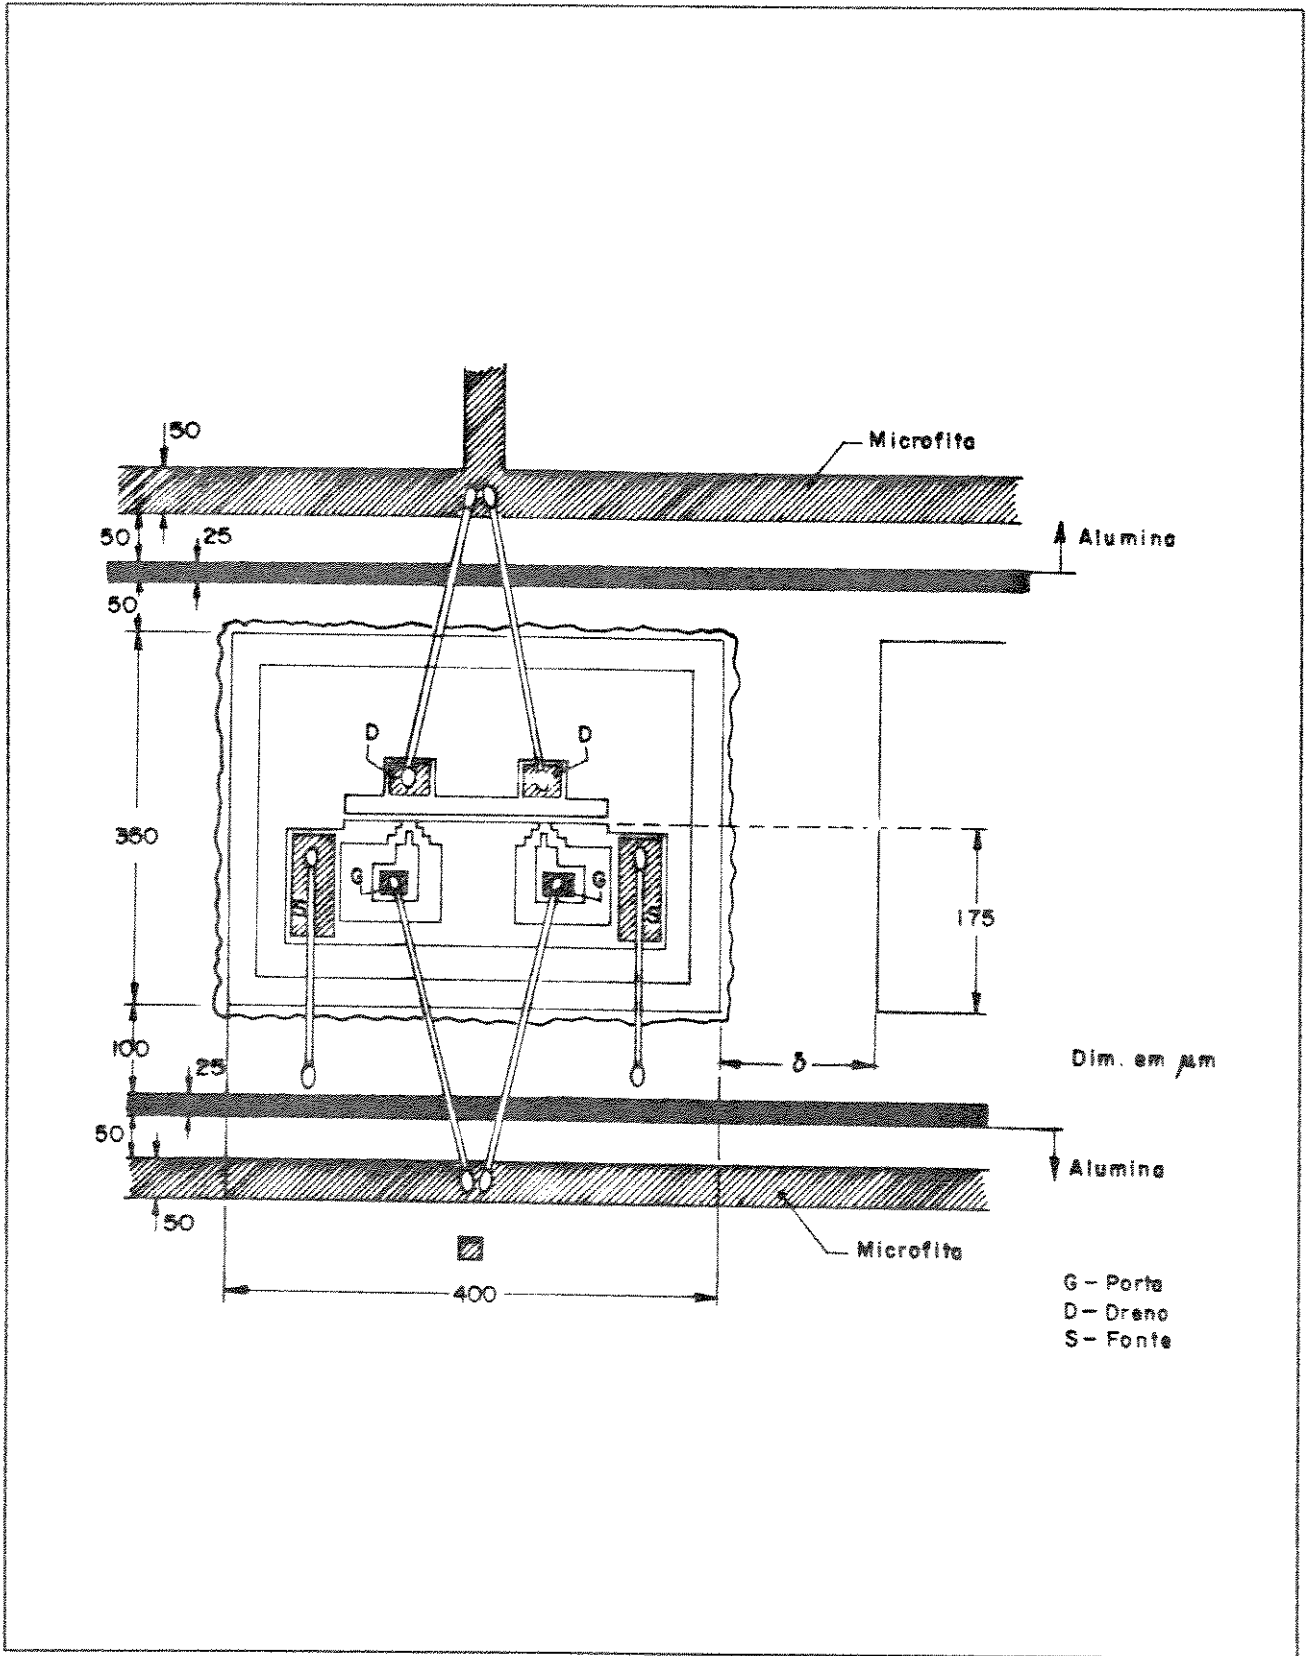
Detalhe das soldas de fios do HEMT NE32100, utilizadas no circuito do AD321.
